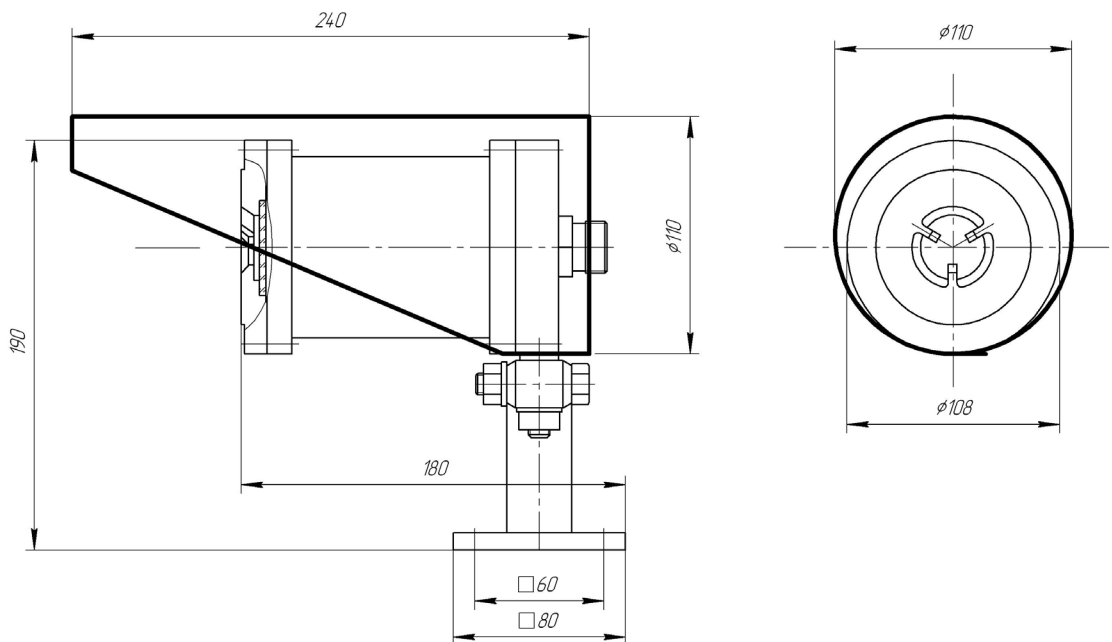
Габаритные размеры извещателя с защитным козырьком
